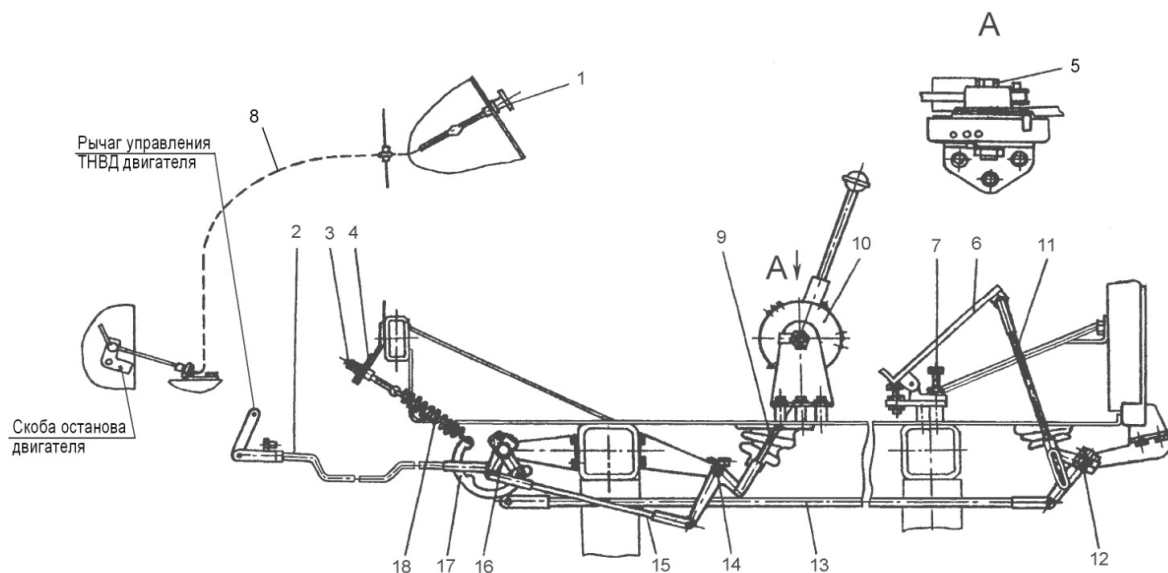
Схема привода управления подачей топлива и останова двигателя
